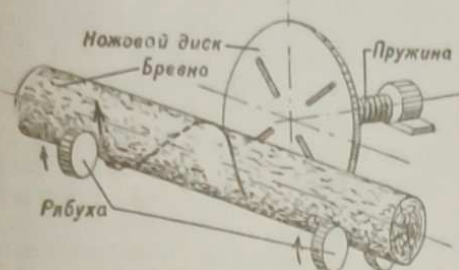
Общая схема станка ЦНИИМЭ-В-2
